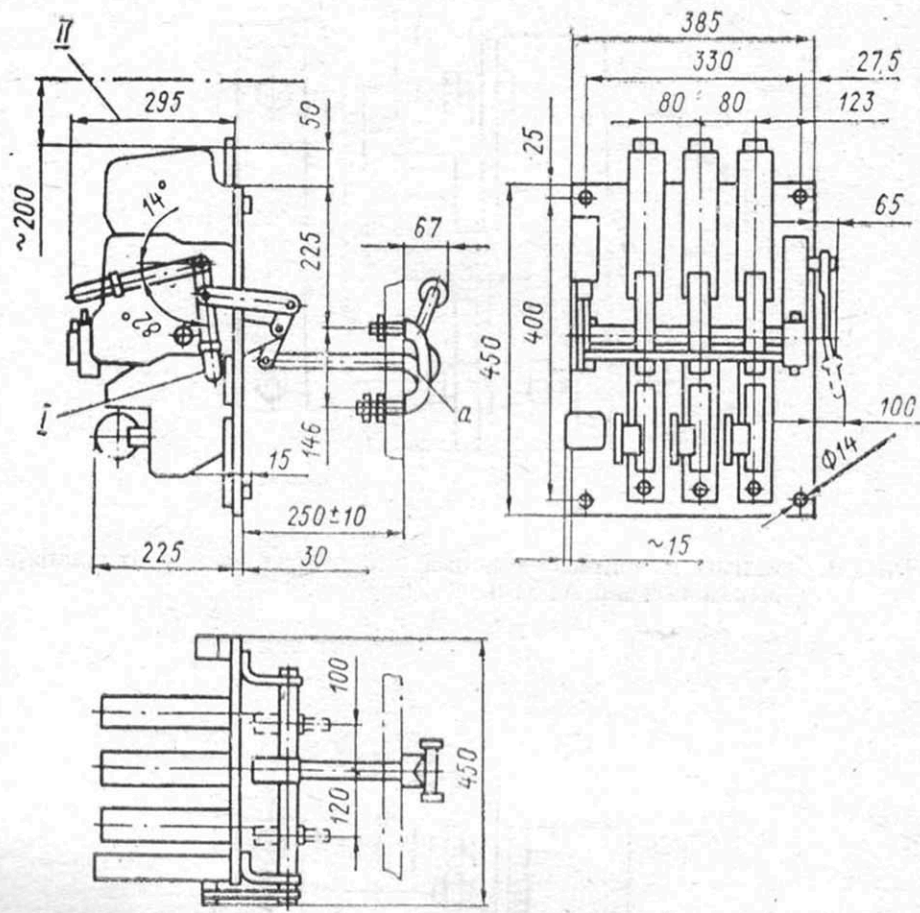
Габаритно-установочные размеры стационарных выключателей с рычажным приводом и рукояткой:
